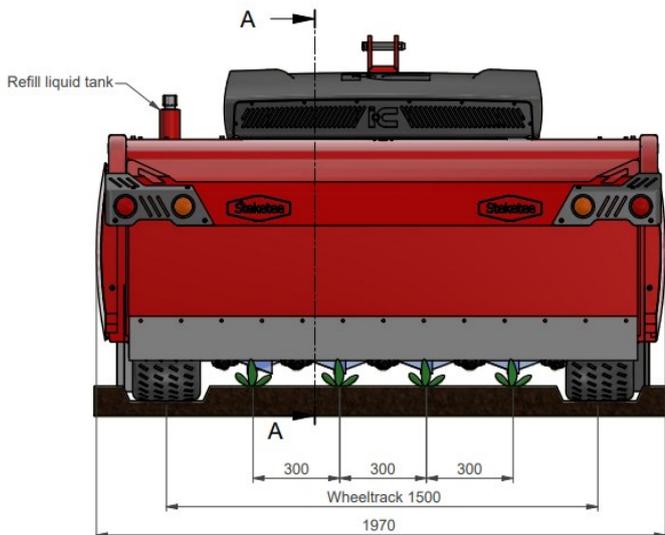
Rückansicht des Prototyps II mit geschlossener Haube. (Quelle: technische Zeichnung von Steketee)
